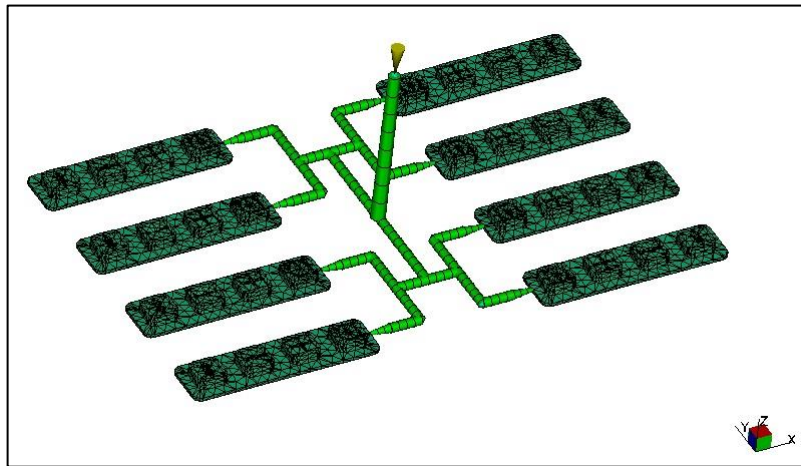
Colocación y mallado del conjunto de piezas y bebedero en moldflow.
